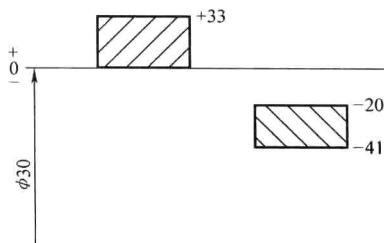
间隙配合尺寸公差带图(偏差单位为 μm)
